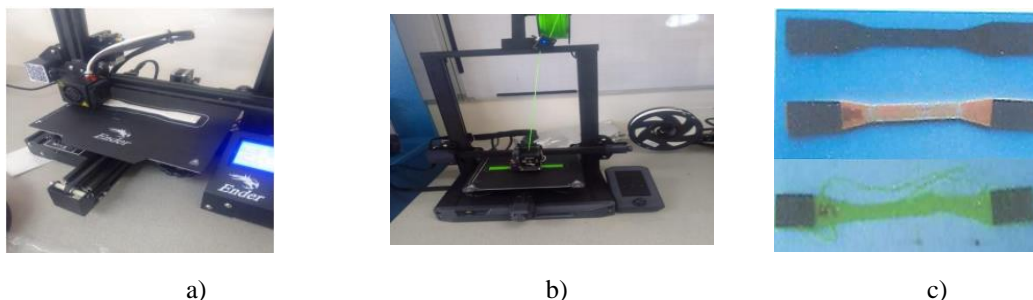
Proceso de impresión en 3D con impresora Ender; a) Impresión de la probeta de material PLA, b) Impresión de la probeta de material TPU y c) Probetas obtenidas mediante la impresión.
